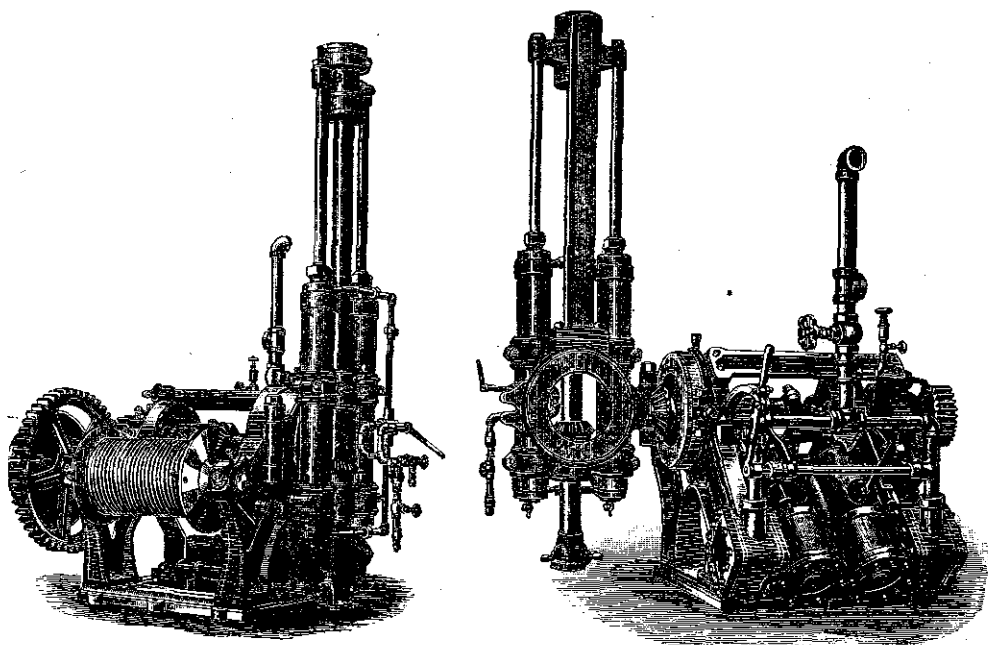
и 110 представляютъ весьма компактно устроенный станокъ для алмазнаго буренія, конструкціи американской фирмы: „Diamond Rock Drill Co“. Штанга приводится во вращательное движеніе двумя цилиндрами, покоющимися на прочной станинѣ, на которой покоится и воротъ для навивки каната при подъемѣ инструмента. Рабочая труба вмѣстѣ съ двумя гидравлическими прессами, служащими для уравновѣшенія всего прибора, укреплена въ общей рамѣ, которая вращается вокругъ массивнаго болта *и*, во время
